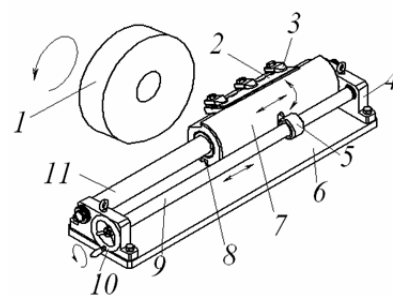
Принципиальная схема устройства для заточки геликоидальных ножей: 1 — шлифовальный круг; 2 — нож; 3 — прихват; 4 — опора с подшипниками; 5 — гайка; 6 — основание; 7 — барабан (несущий цилиндр); 8 — ролик кулачка барабанного типа; 9 — винт; 10 — маховичок; 11 — направляющая барабана
